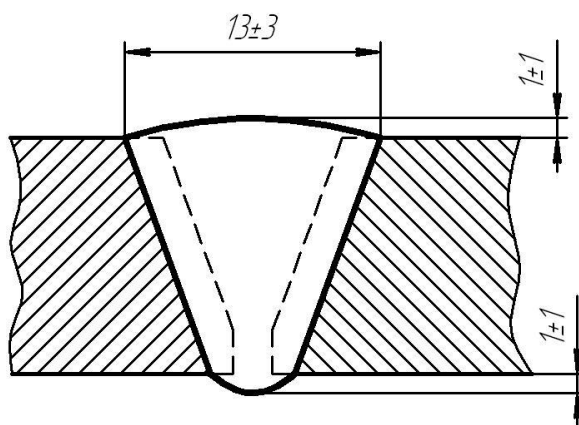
Геометрия сварного шва при заварке трещины
